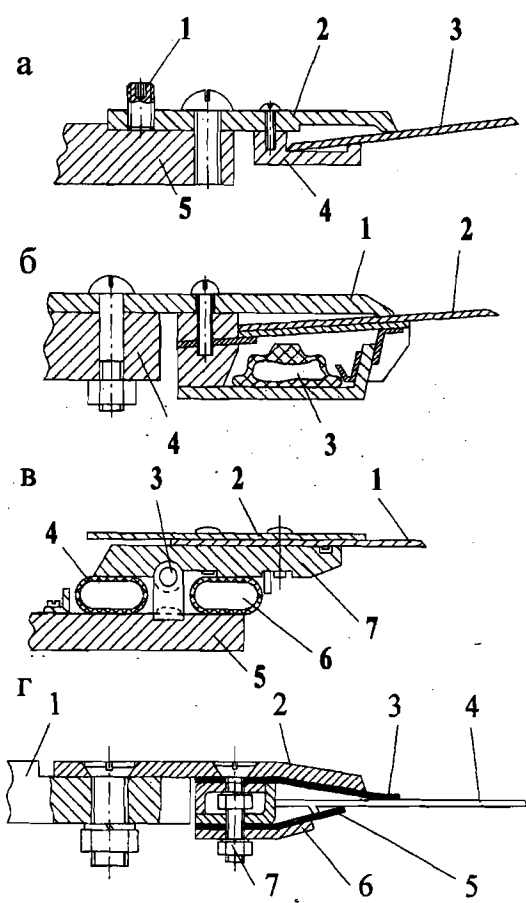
Держатели шаберов: а – Accumate: 1 – регулировочный винт; 2 – верхняя губа; 3 – лезвие; 4 – нижняя губа; 5 – балка шабера; б – Conformatic: 1 – верхняя губа; 2 – лезвие; 3 – пневмокамера; 4 – балка шабера; в – DST: 1 – лезвие; 2 – пластина; 3 – ось вращения; 4, 6 – пневмокамеры; 5 – балка шабера; 7 – плита; г – ООО «Шаберные лезвия»: 1 – балка шабера; 2 – верхняя губа; 3 – верхняя пружина; 4 – лезвие; 5 – нижняя губа; 6 – нижняя губа; 7 – гайка регулировочная
